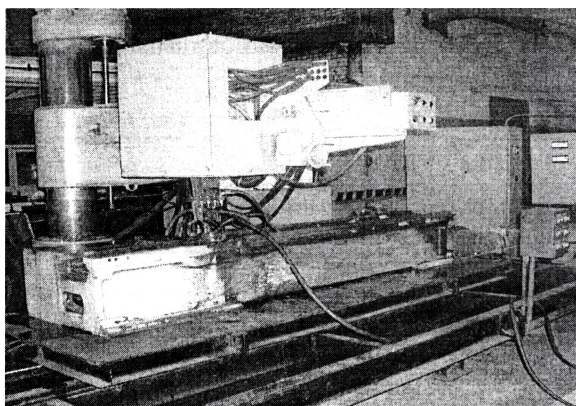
Индукционная установка для закалки ТВЧ направляющих станин металлорежущих станков
